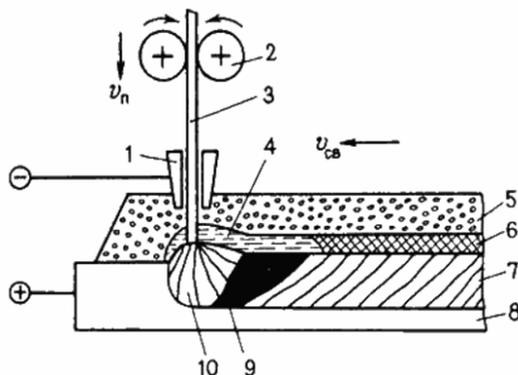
Схема механизированной наплавки металла под слоем флюса:
